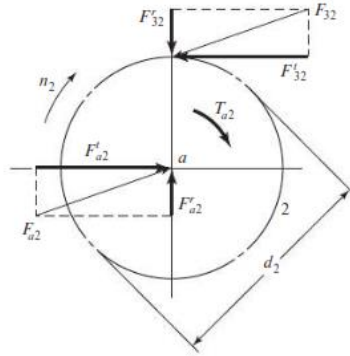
Descomposición de fuerzas en un engranaje recto [12].
